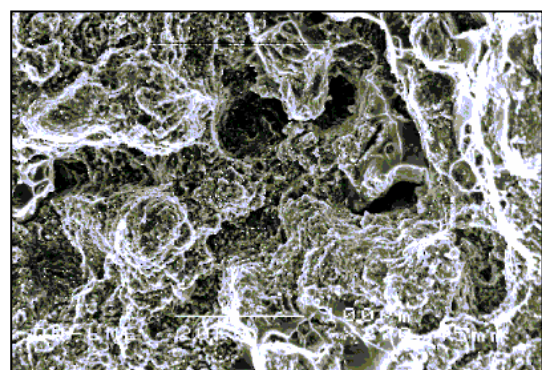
Fractografía de la probeta 1-C4, fractura dúctil; buen comportamiento a tracción.
